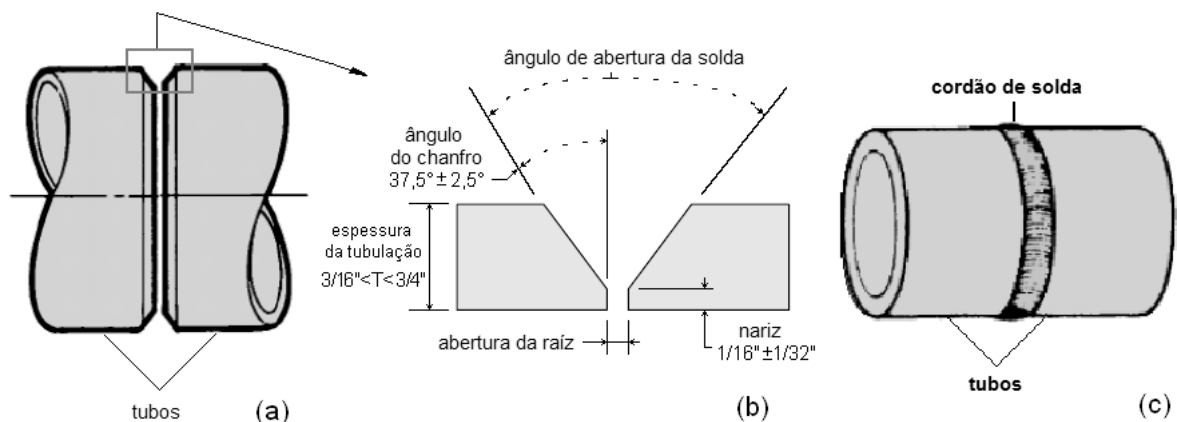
(a) Tubos a serem soldados; (b) Secção transversal de junta com chanfro em V; (c) Tubos unidos através da execução do procedimento de soldagem.
